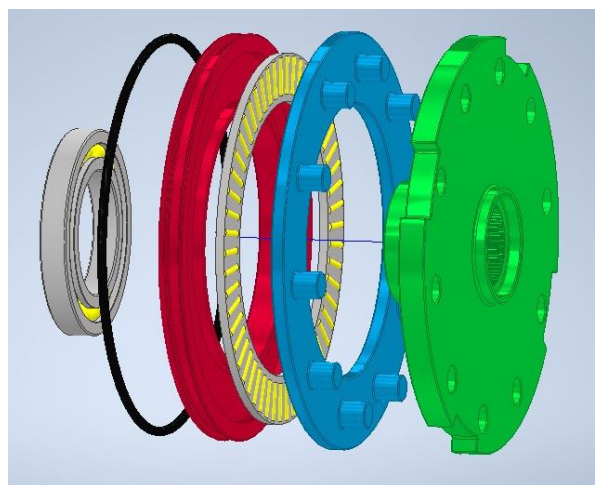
Vista Explodida Componentes Pistão Embraiagens
